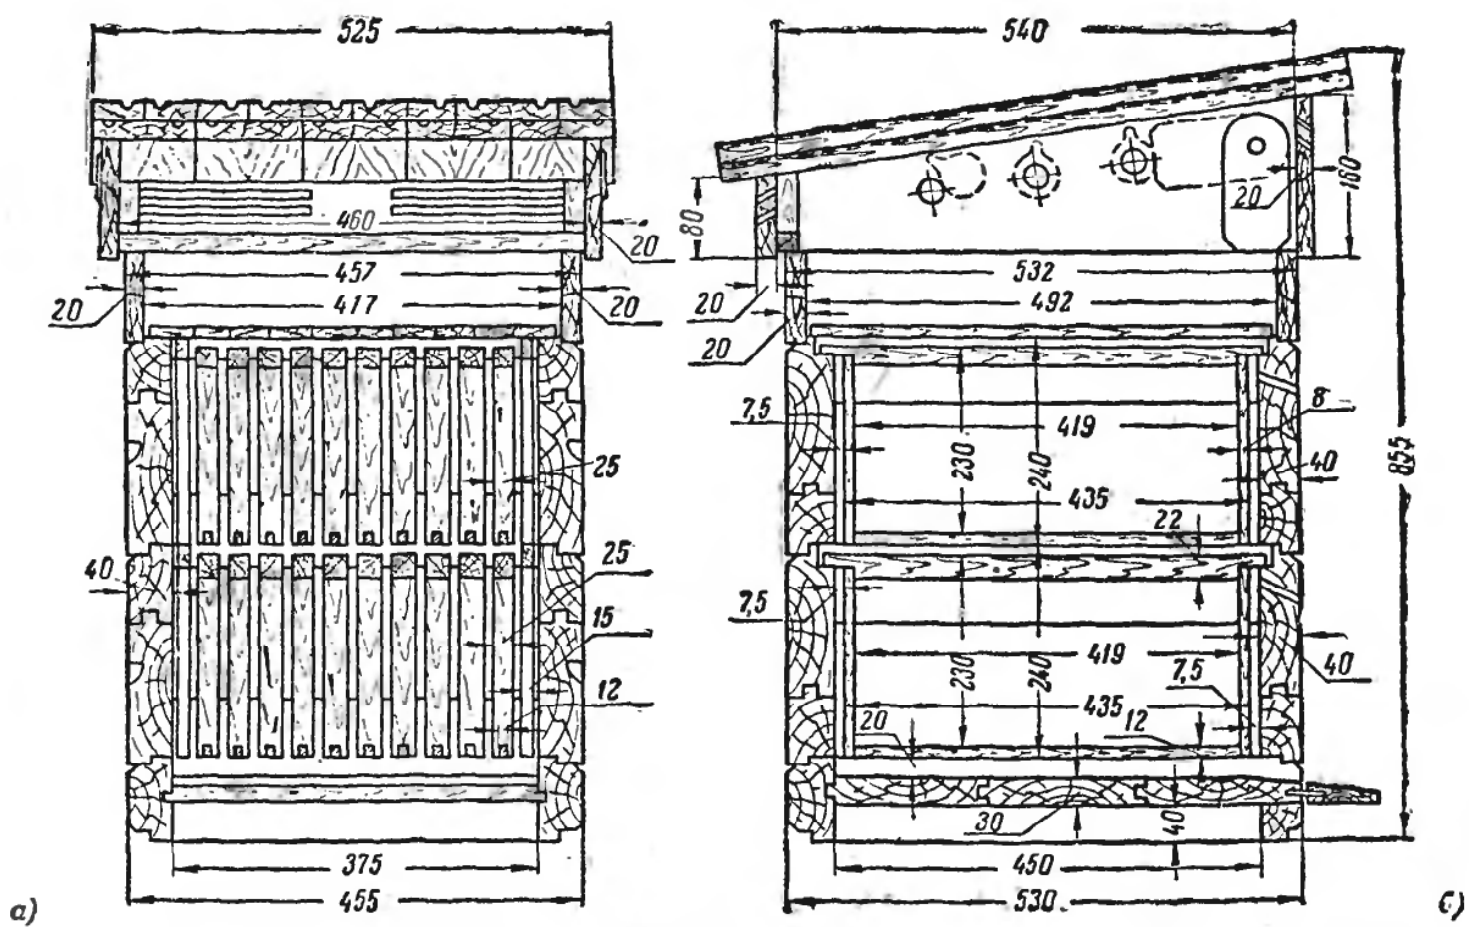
а. Одностенный 10-рамочный улей Рута с двумя корпусами: слева — поперечный разрез; справа — продольный разрез.
